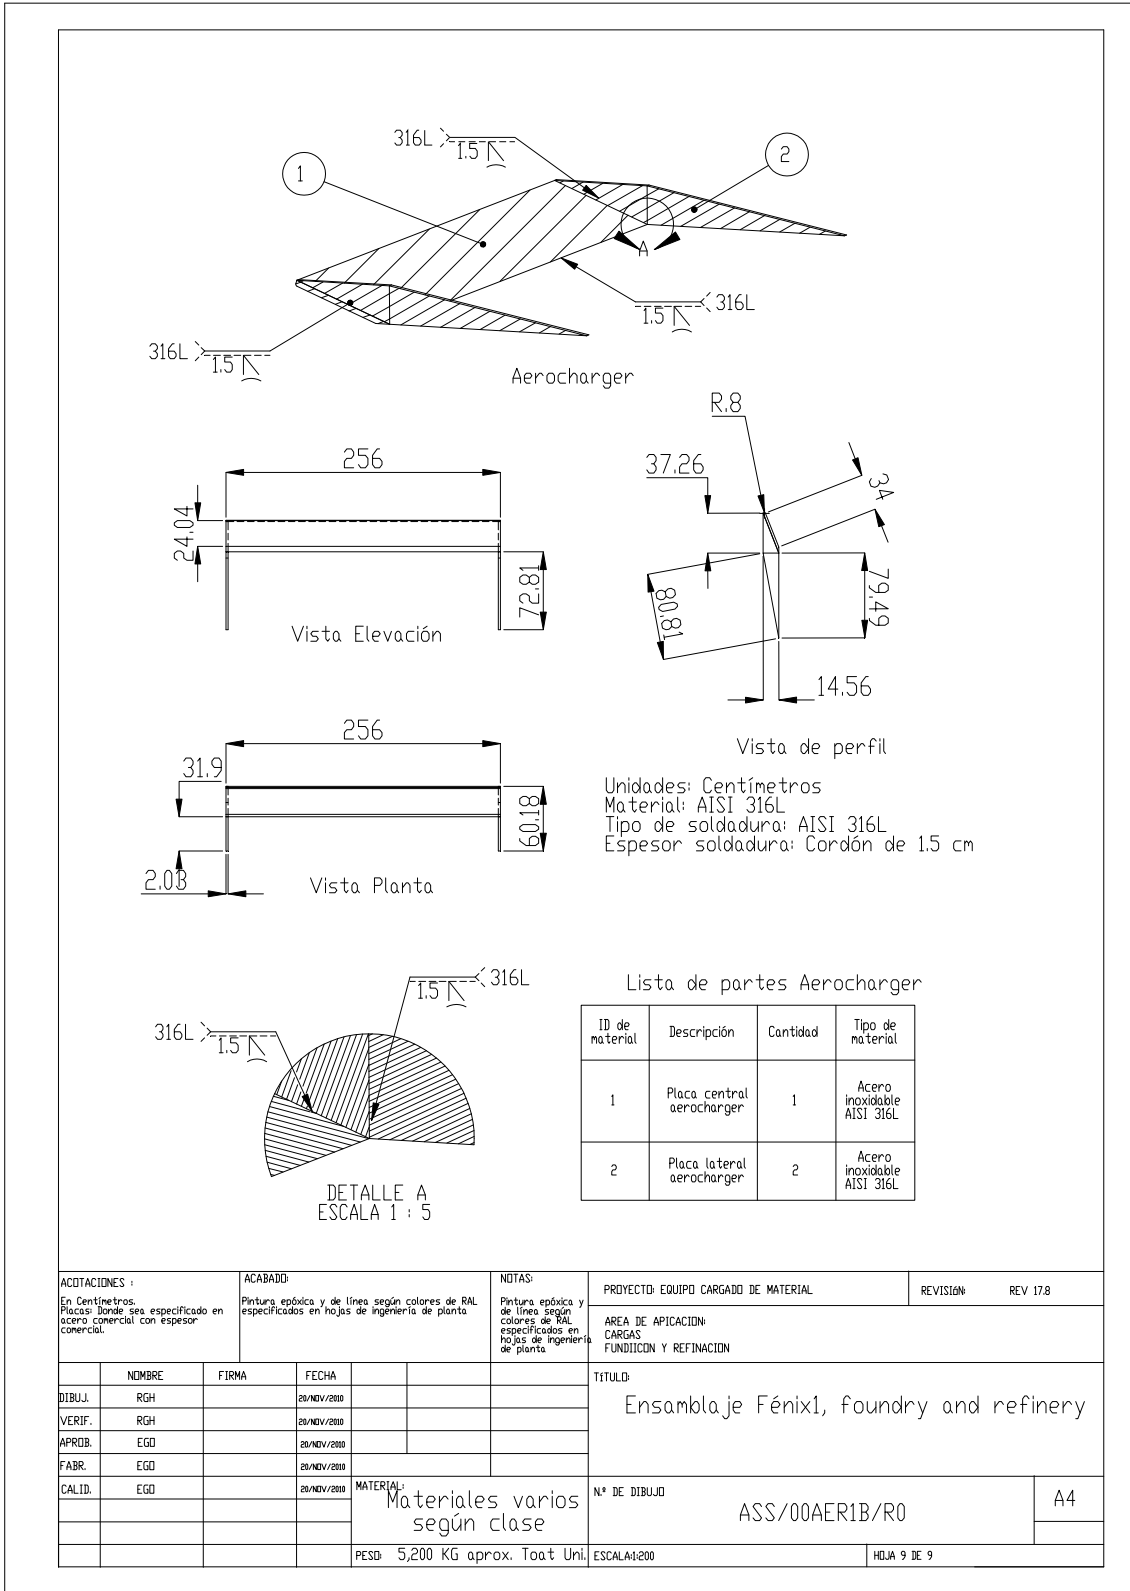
Despiece general del aero charger. Ensamble de unidad.
